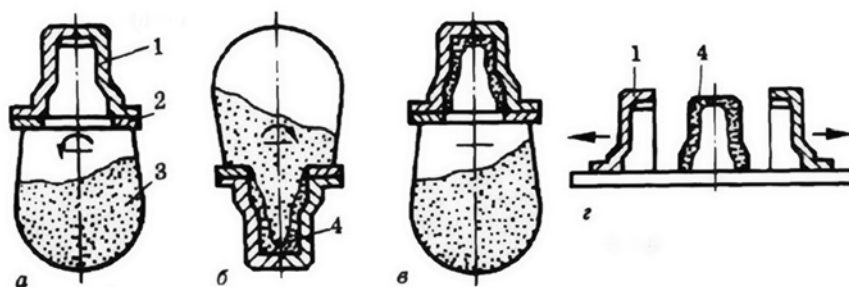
Схема бункерного способа изготовления оболочкового стержня
